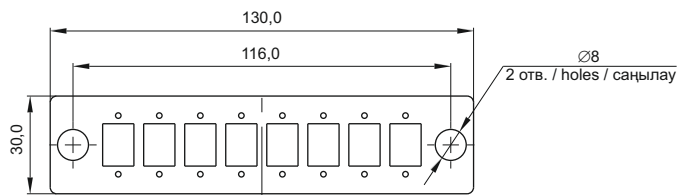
Габаритные и установочные размеры панели FOBX-P08-SC-R / Figure 3 – Overall and mounting dimensions of the panel FOBX-P08-SC-R / 3 сурет – FOBX-P08-SC-R панелінің габариттік және орнату өлшемдері
